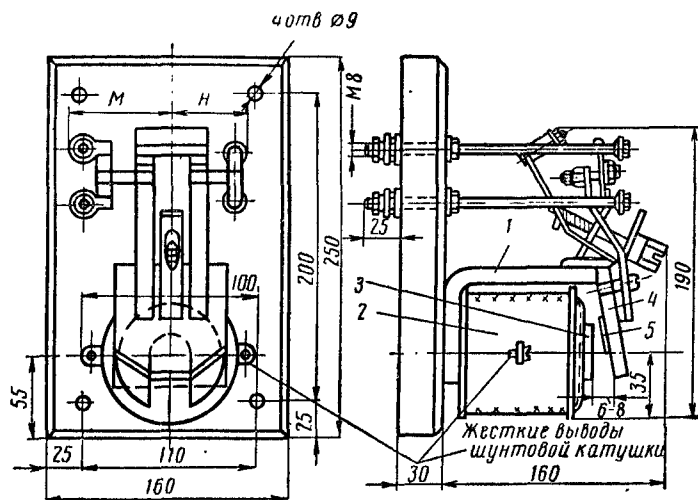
Общий вид и габаритные размеры реле времени постоянного тока РЭ-180 и ЭРЭ-180
